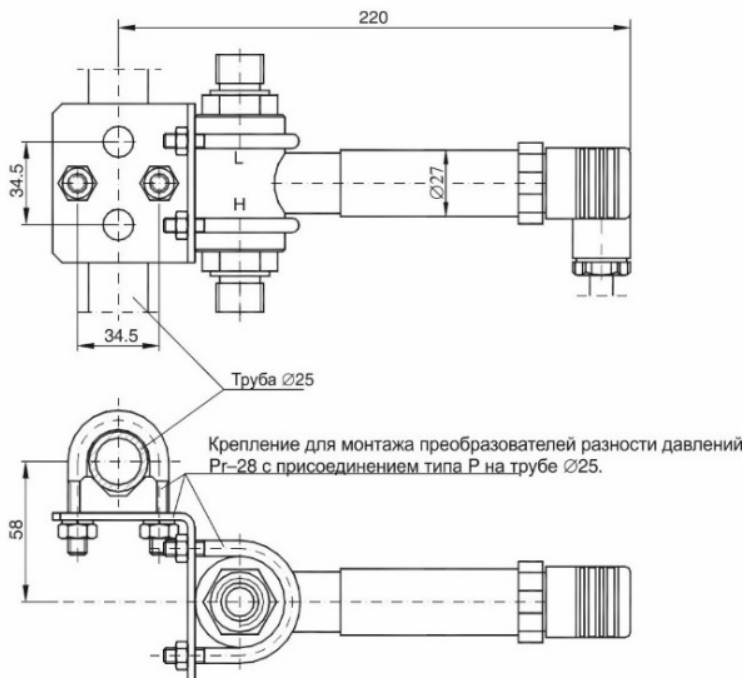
Преобразователь PC-28P. Габаритные размеры.
